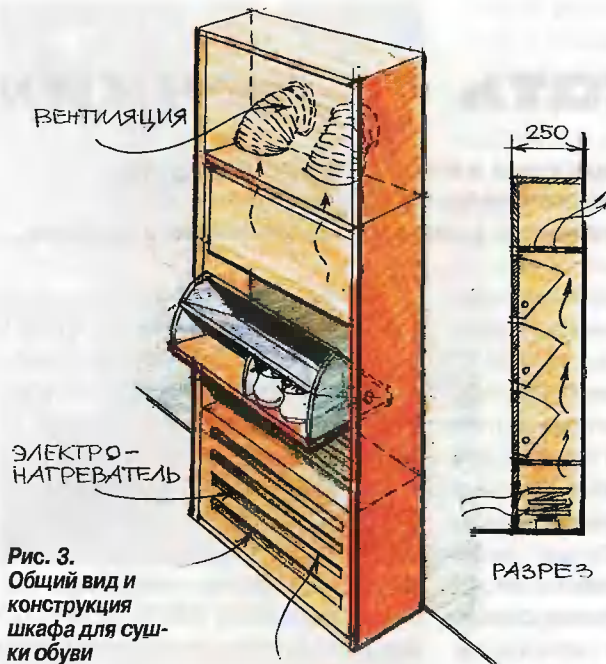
Общий вид и конструкция шкафа для сушки обуви
